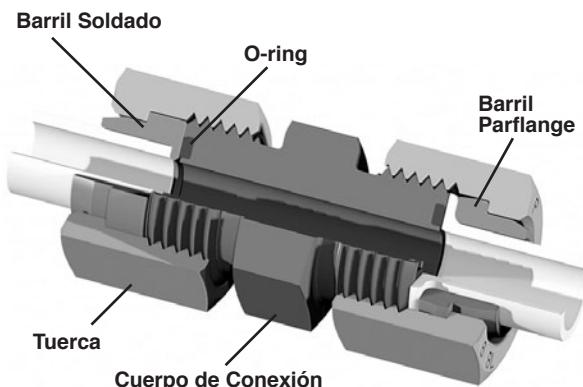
Corte de la Unión Seal-Lok Union, con el Parflange ensamblado y soldado
